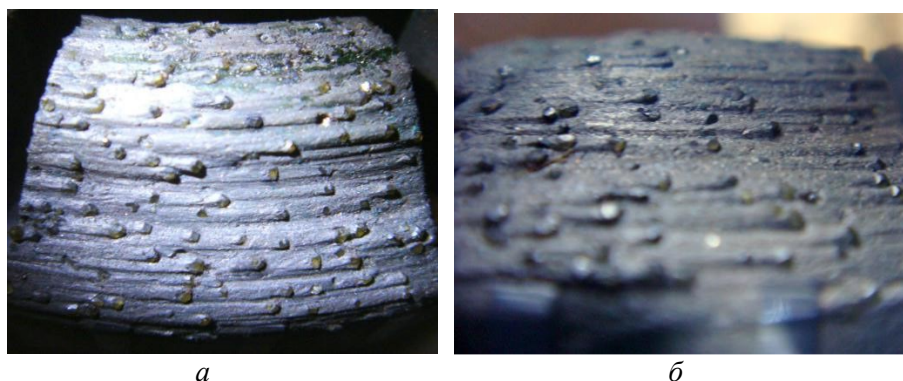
Характерный внешний вид участка рабочего торца коронки, оснащенной металлизированными алмазами: *а* – вид сверху; *б* – вид сбоку
